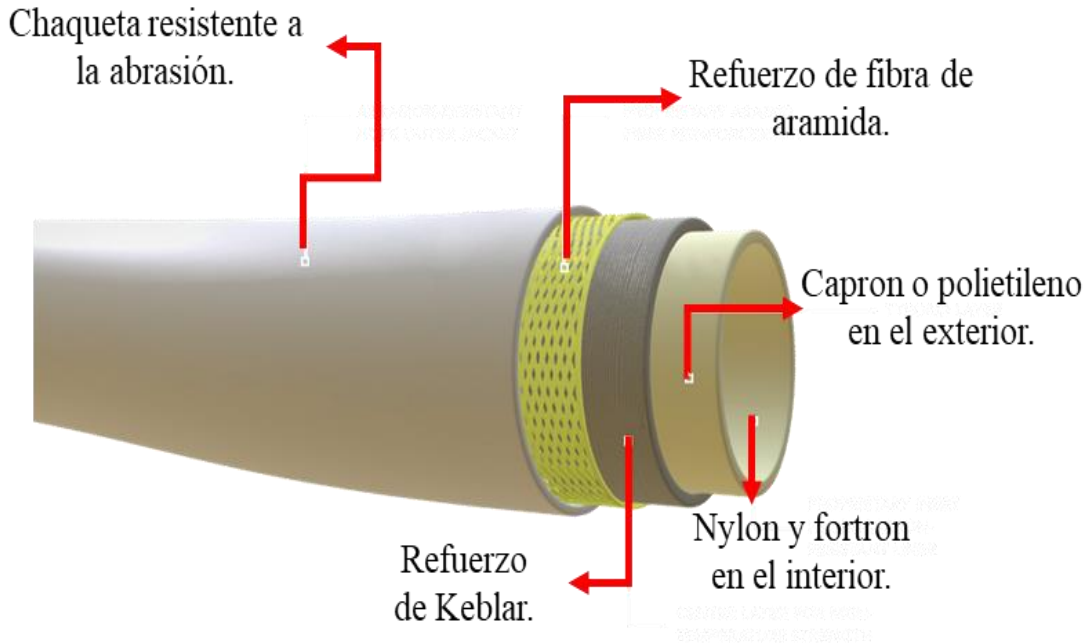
Tubería *Fiberspar*, modelo constructivo
